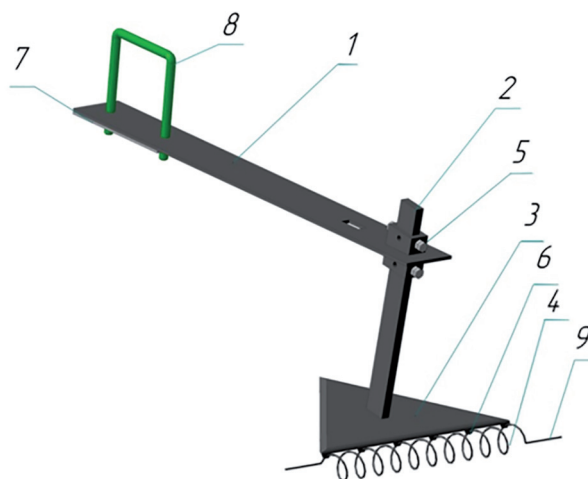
3D-модель секции культиватора со спиральными лапами: 1 – пружинный грядиль; 2 – стойка; 3 – треугольный лемех; 4 – спираль; 5 – держатели; 6 – зацеп; 7 – упорная пластина; 8 – скоба; 9 – струна
